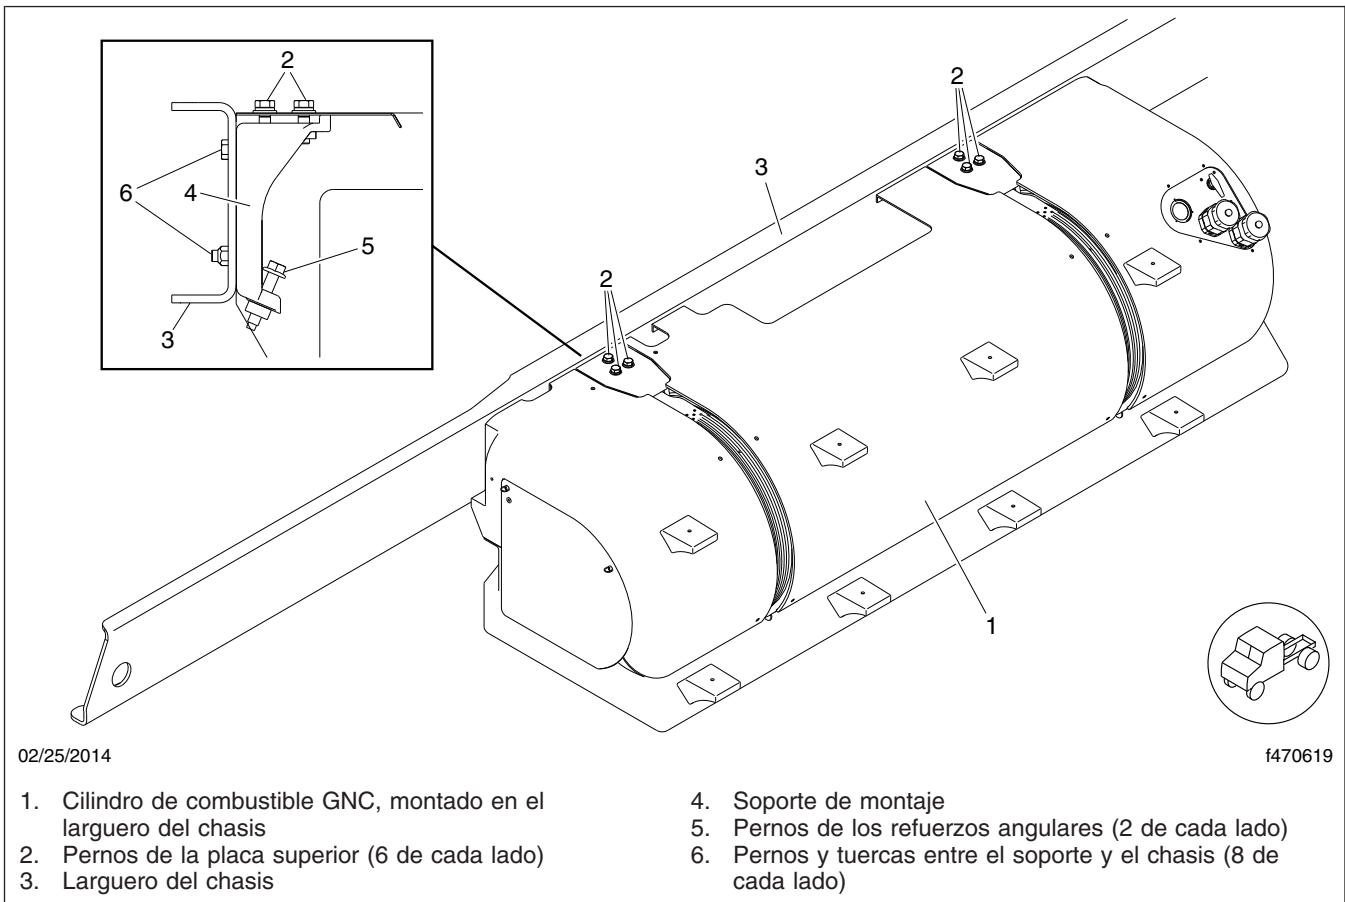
, Soporte de montaje del cilindro de combustible (tanque montado en el larguero)
